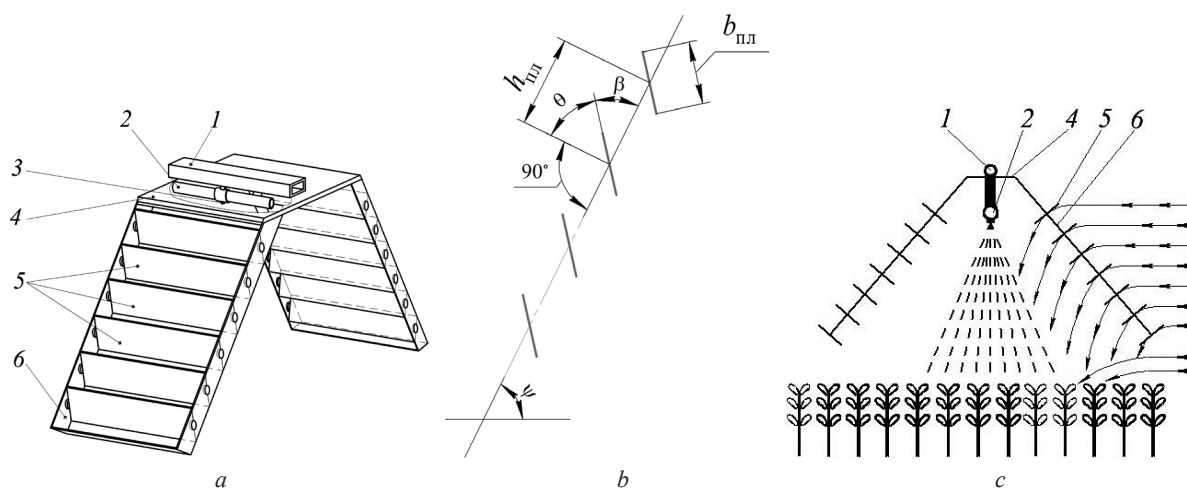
Ветрозащитное устройство комбинированного действия: *a* – схема; *b* – конструктивные параметры; *c* – рабочий процесс; 1 – несущая конструкция; 2 – распределительная штанга; 3 – распылитель; 4 – кронштейн; 5 – прямоугольные пластины (жалюзи); 6 – рамка
